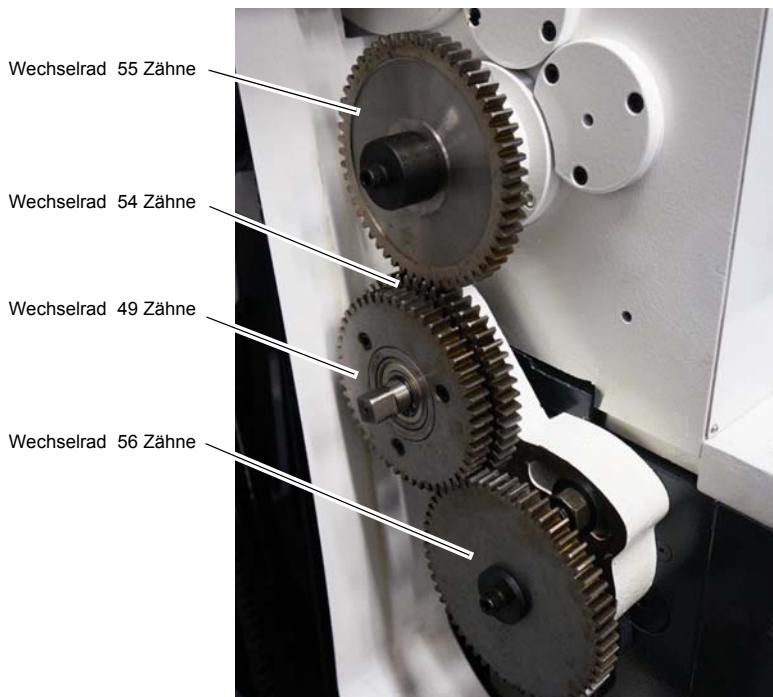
Wechselradposition für Metrische - und Zollgewinde
